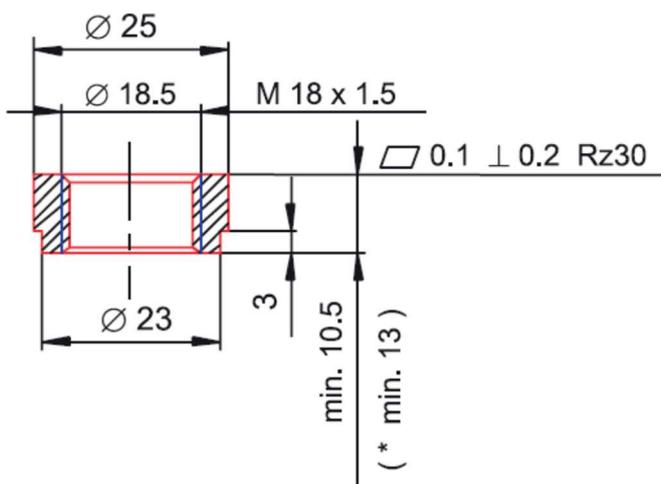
FIXAÇÃO DA SONDA (PORCA SOLDADA), FONTE: DATASHEET DO FABRICANTE.
